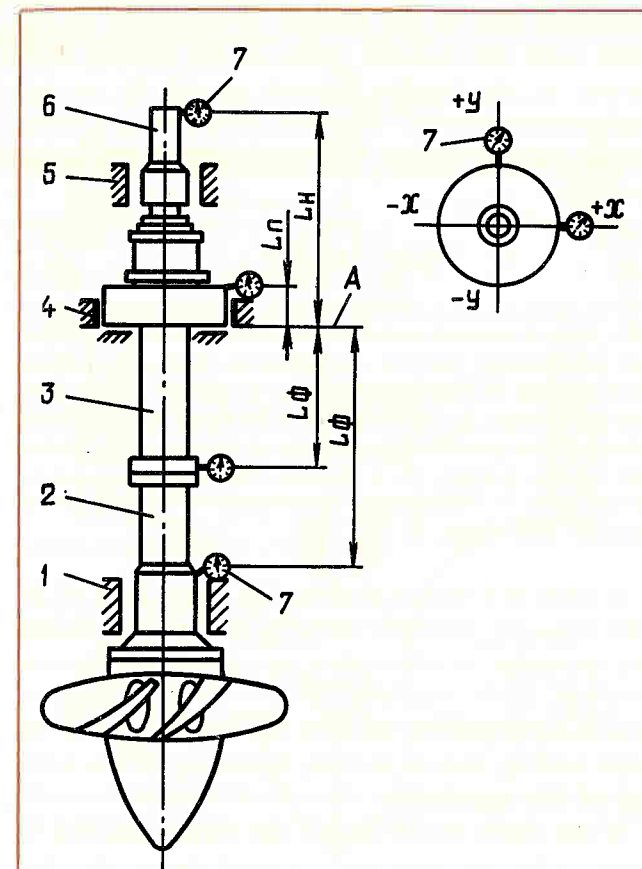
Схема проверки общей линии вала гидроагрегата:
